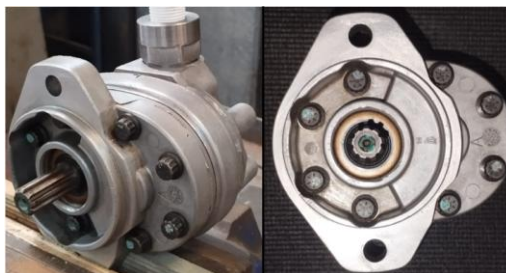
Desmontaje y desconexión de la bomba hidráulica
